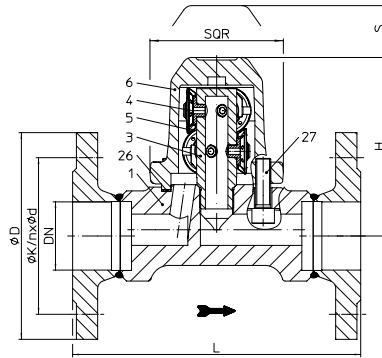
1....6K2 (DN40-50) mit 6 Kapseln, mit Flanschen
